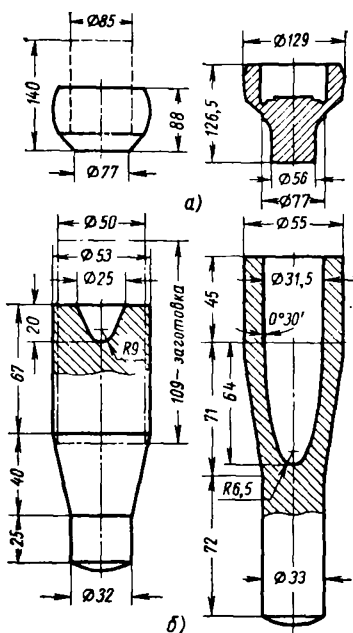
Двухпереходная штамповка поковки с глухой полостью: а — звездочки дифференциала; б — стакан
